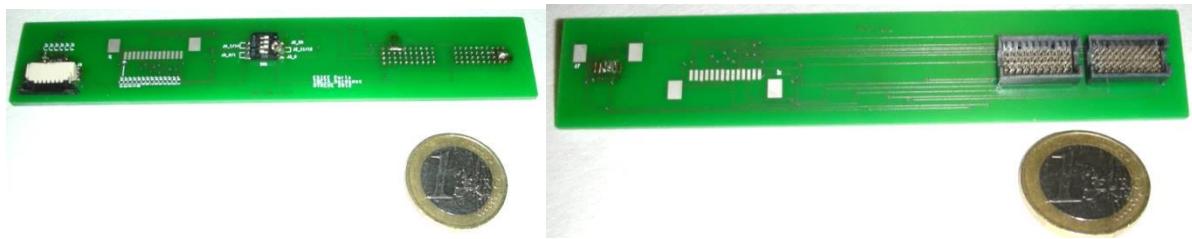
PCB de connexion (vue recto et verso) pour des implants rétiniens
